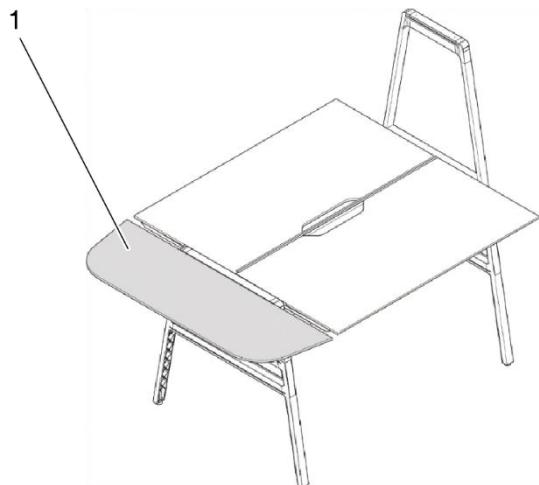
Piastra da montaggio esterno trapezoidale, montaggio consentito
